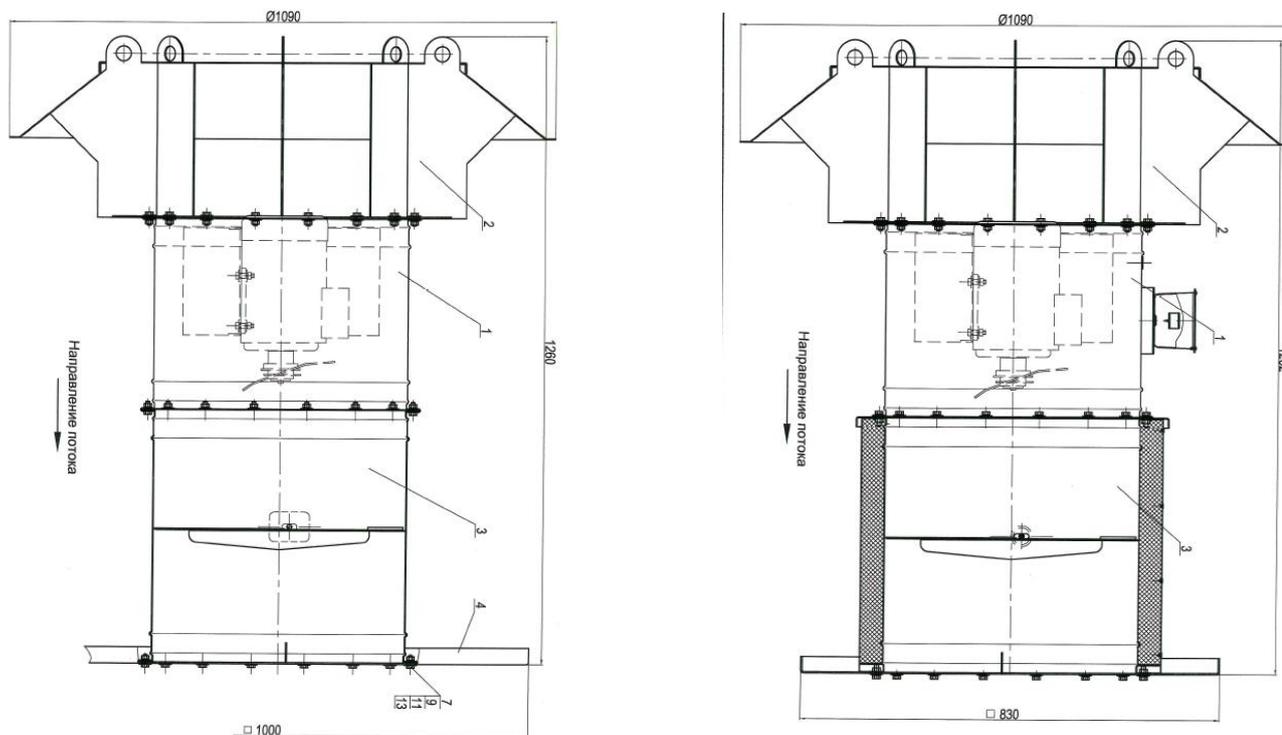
Габаритно присоединительные размеры ВКОПв 13-284
